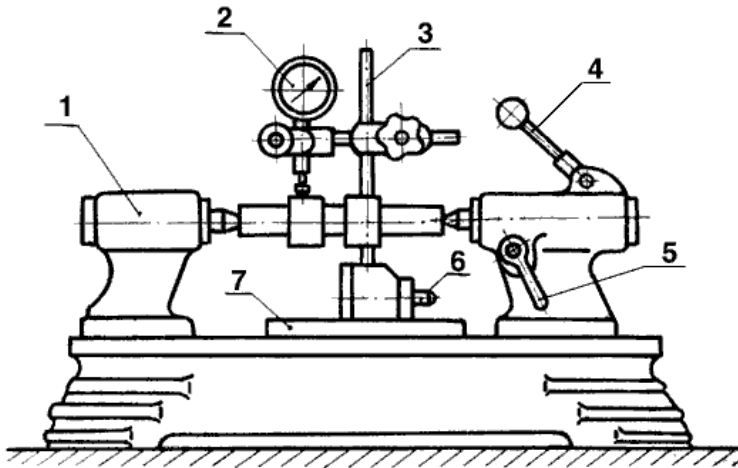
Схема перевірки радіального биття шийки вала: 1 – прилад; 2 – індикатор годинникового типу; 3 – штатив; 4 – рукоятка; 5 – затискач; 6 – кнопка керування магнітом; 7 – стіл
